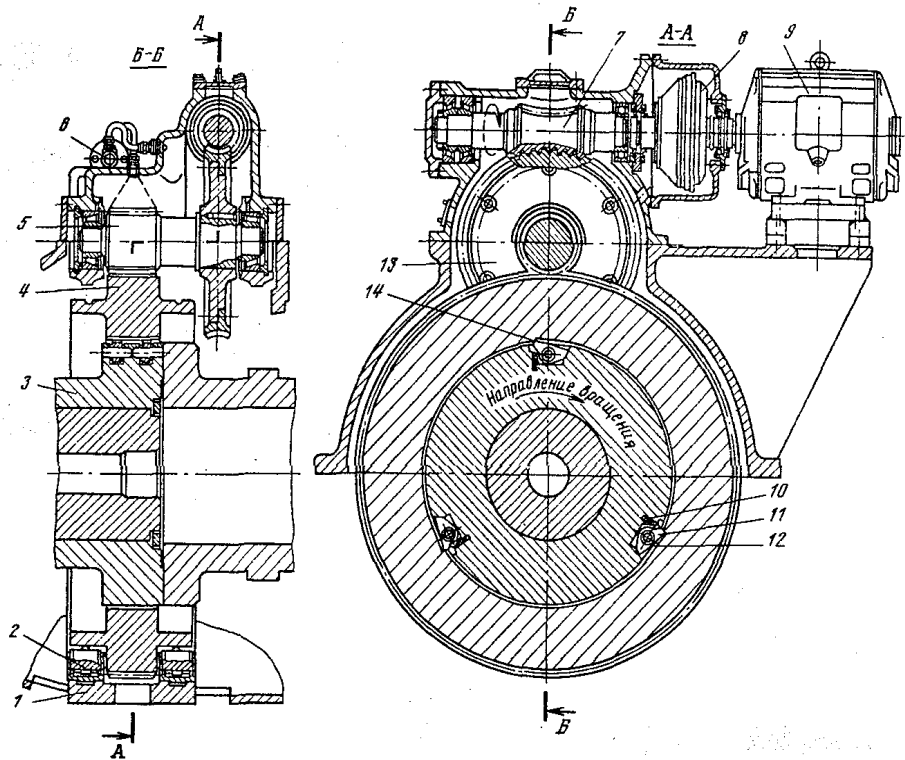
Валоповоротний пристрій турбіни АЕС виробництва ХТЗ:
